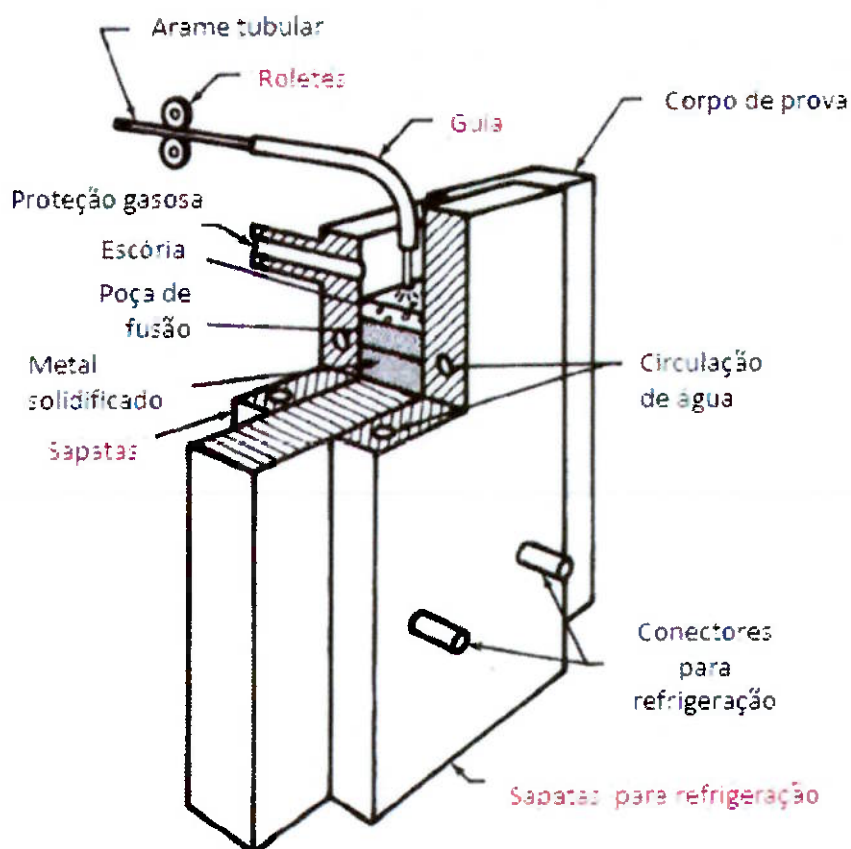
6 - Dispositivos para soldagem EGW. [5]
